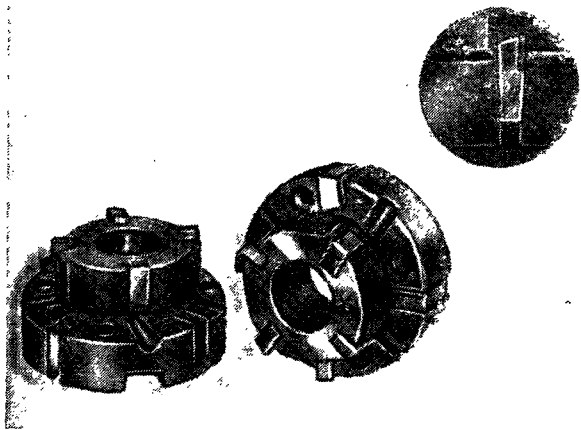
Сборные двухступенчатые зенкеры со вставными ножами
